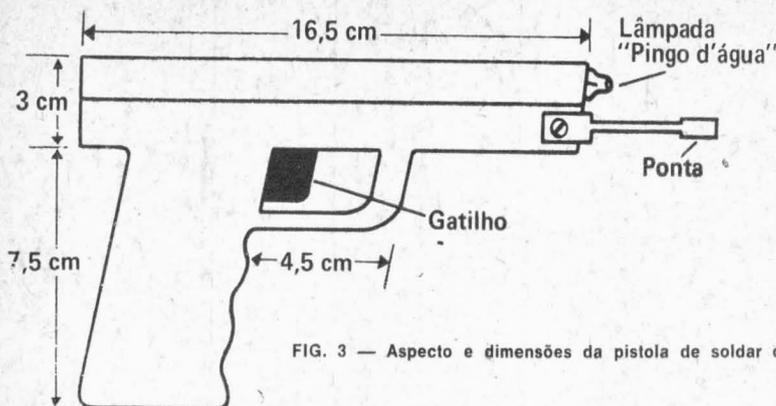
Aspecto e dimensões da pistola de soldar descrita no texto.
